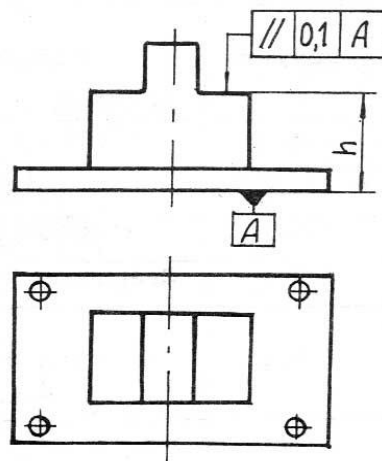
Схема установки заготовки на консольно-фрезерном станке
